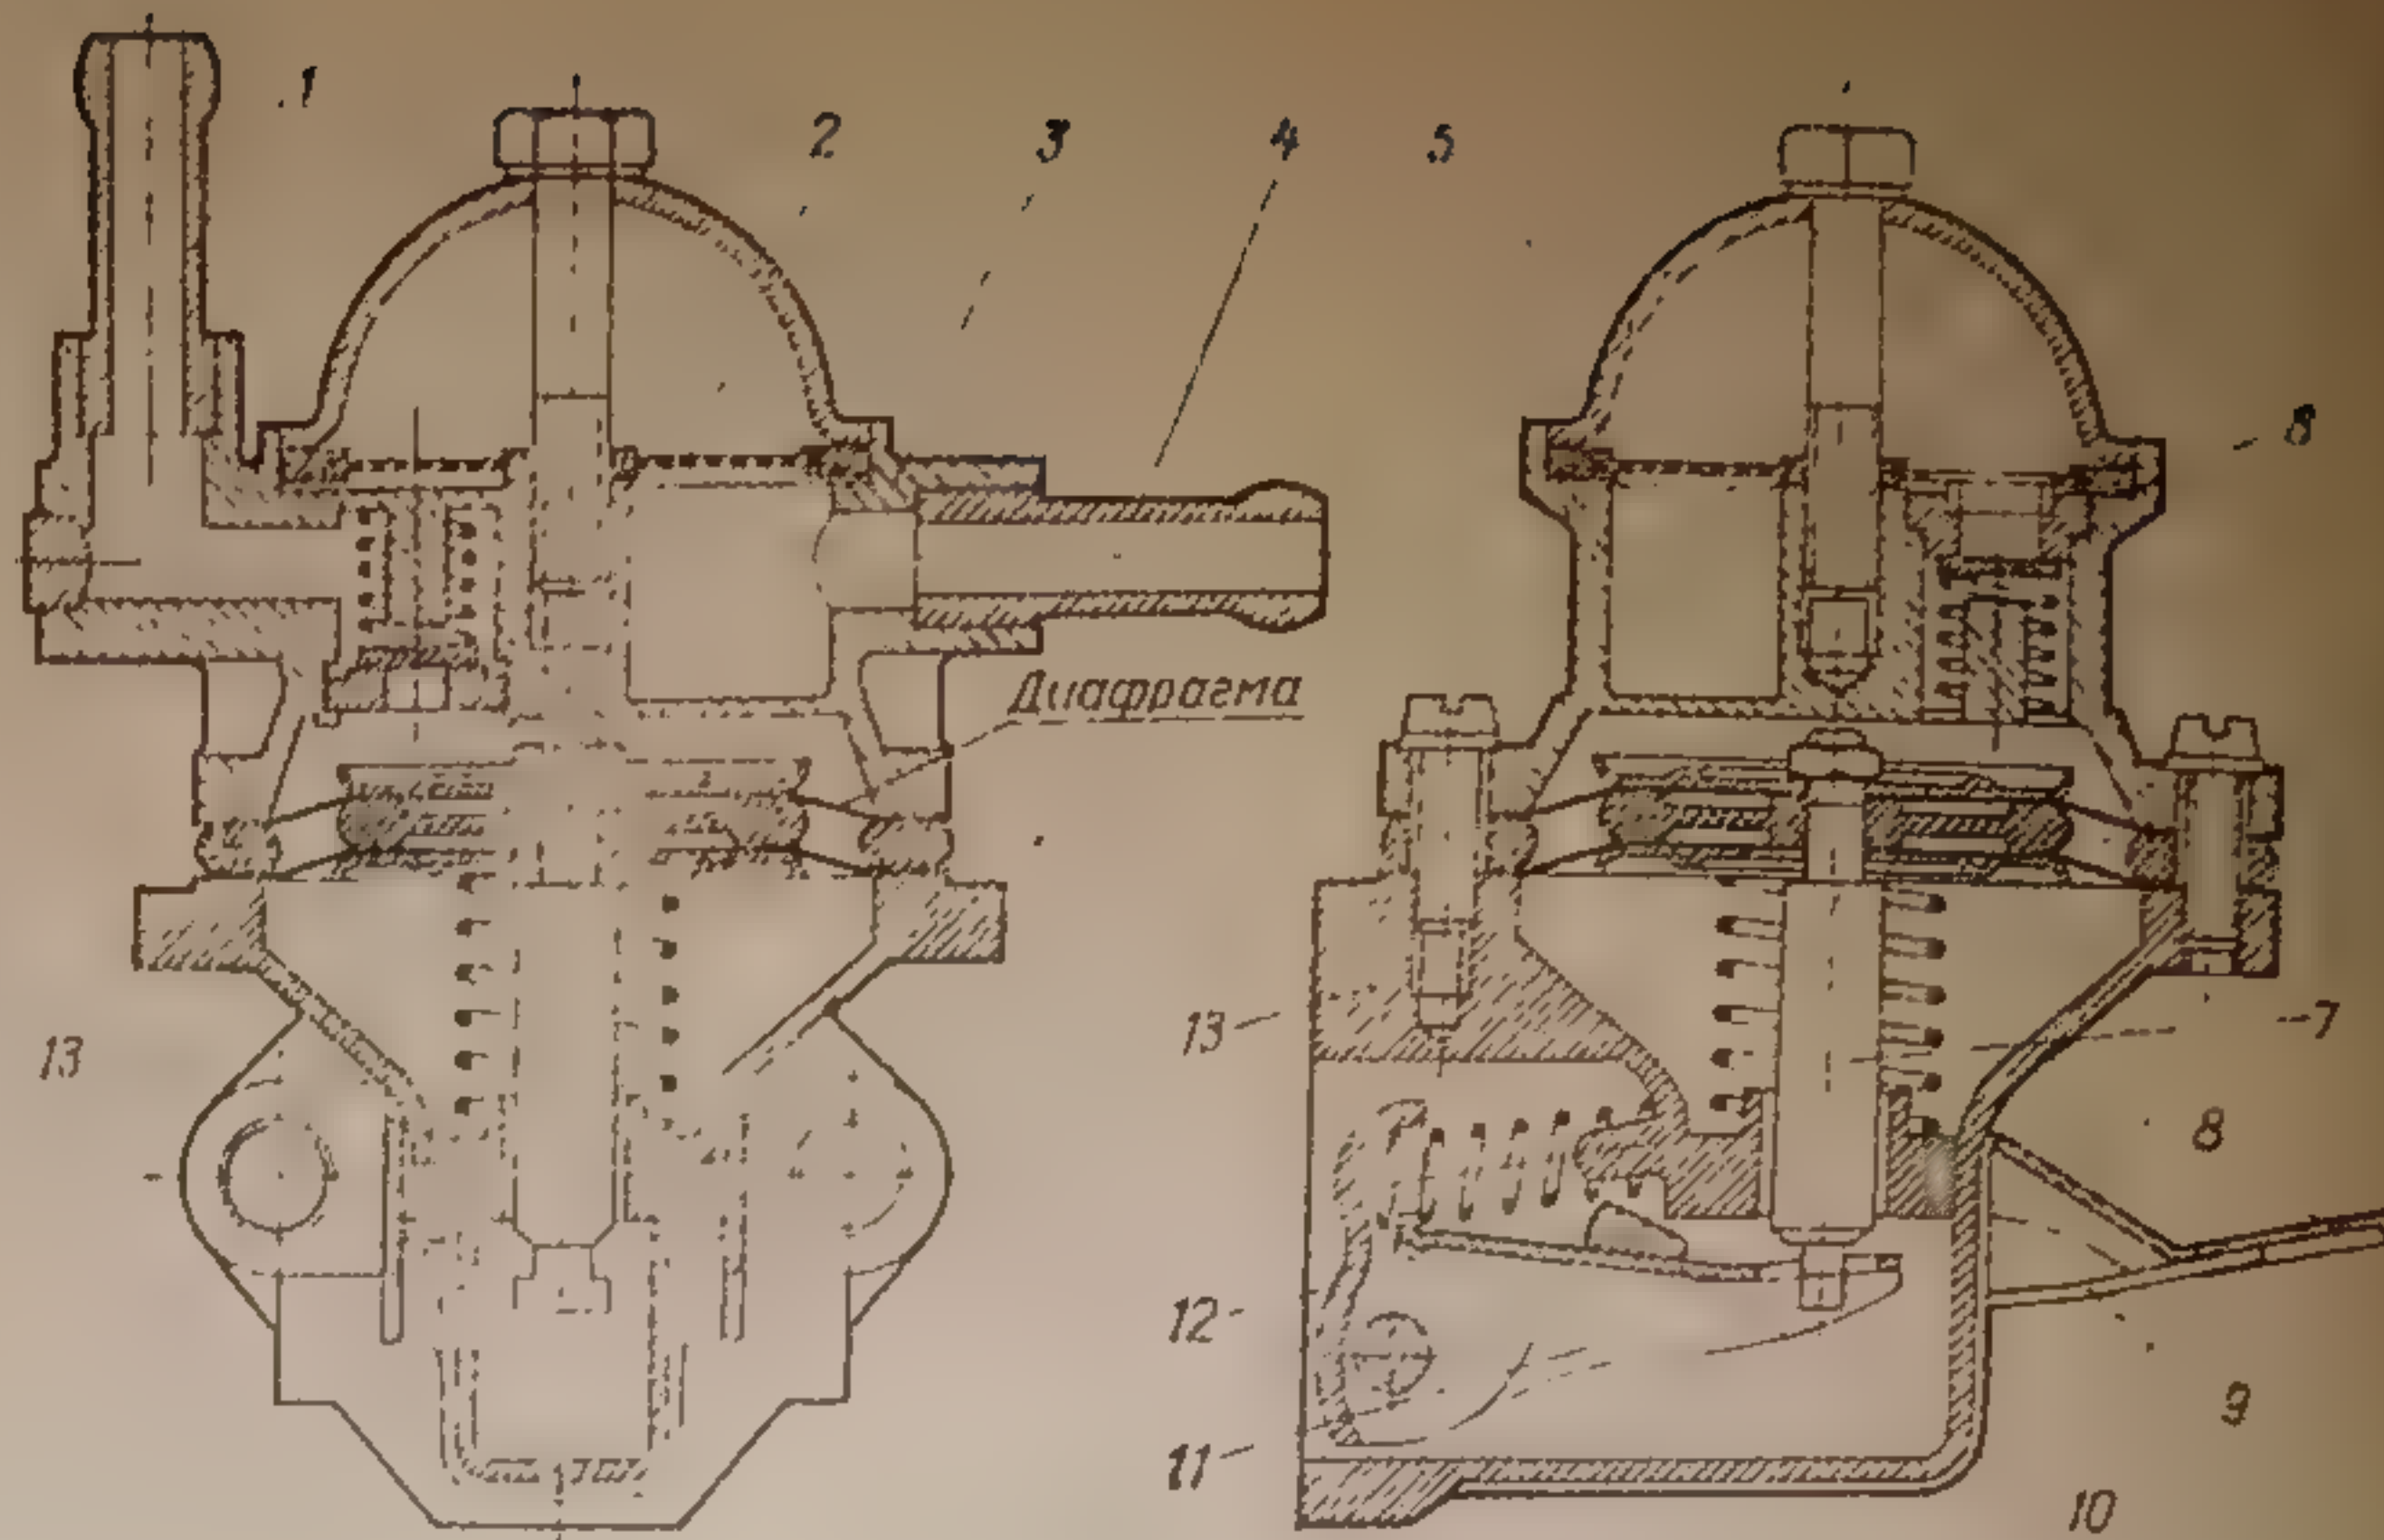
Топливный насос автомобилей: 1 — нагнетательный патрубок; 2 — сетчатый фильтр; 3 — верхний корпус; 4 — всасывающий патрубок; 5 — крышка; 6 — клапан всасывающий; 7 — тяга, 8 — рычаг ручной подкачки топлива; 9 — пружина; 10 — кулачок; 11 — балансиры; 12 — рычаг механической подкачки топлива; 13 — нижний корпус
